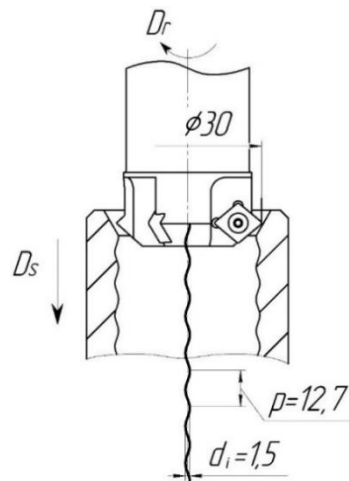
Схема оброблення круглої внутрішньої різі непрофільним інструментом
